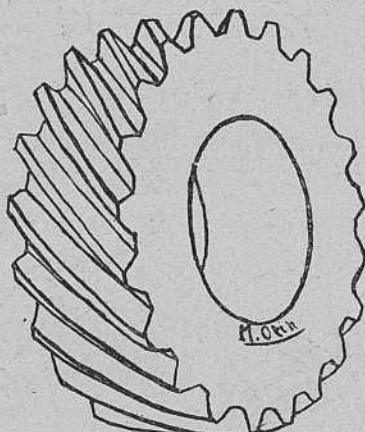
Engranaje helicoidal en el que se desea conocer el ángulo de inclinación del diente.
